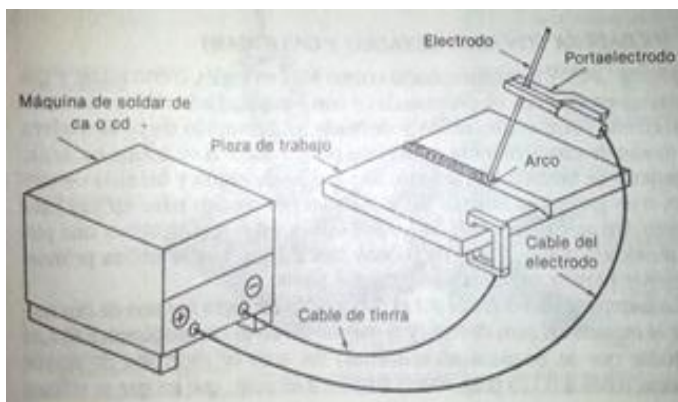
Equipo para realizar soldadura eléctrica.
